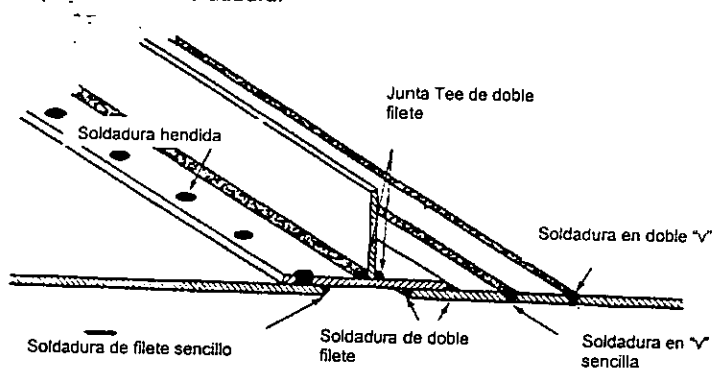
Soldadura en elementos estructurales
